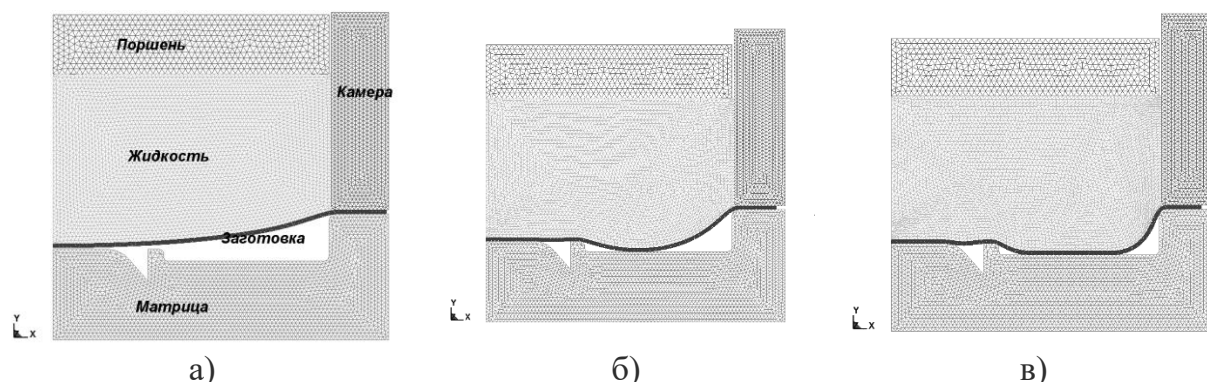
Взаимодействие заготовки с матрицей при наличии жидкости: а) заготовка до соприкосновения с рельефом матрицы, б) соприкосновение заготовки с матрицей, в) заполнение рельефа матрицы
